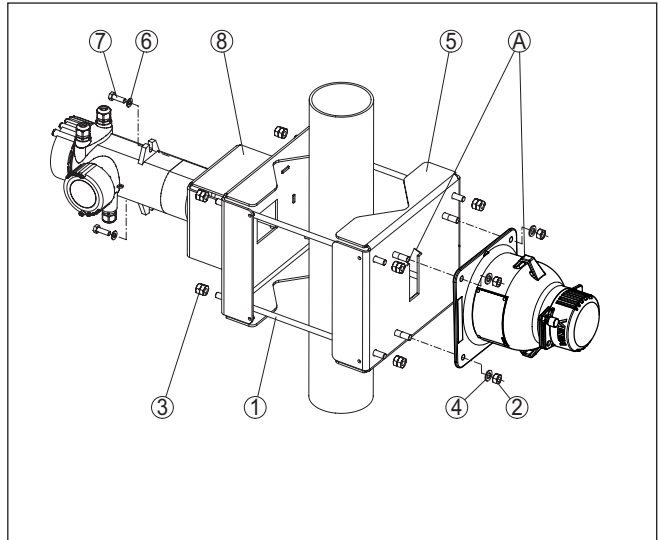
Dispositivo de sujeción con sensor montado horizontalmente (con VEGASOURCE 81, 82, 83)
